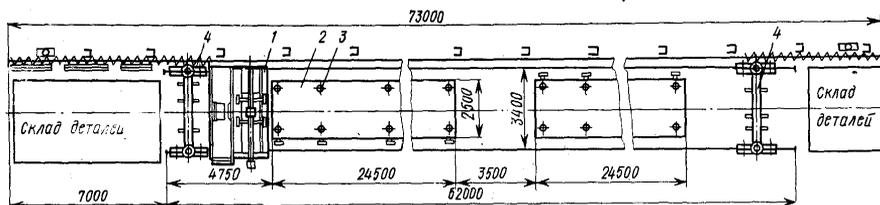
Схема участка для сборки и сварки плоских вагонных конструкций
